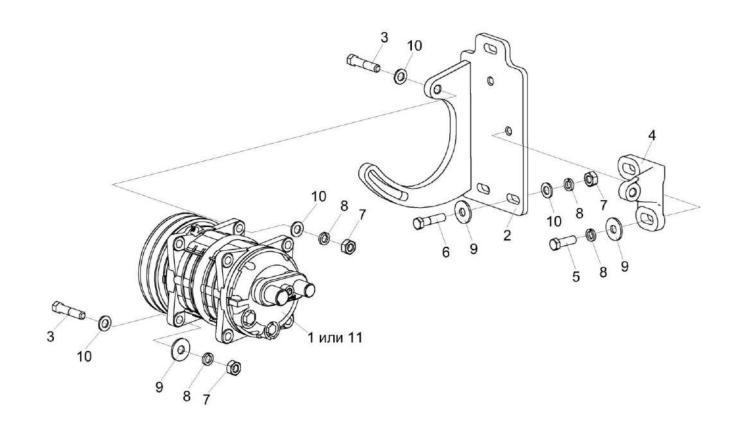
Установка компрессора КВС-7-0121030ВИ1 и КВС-80-7-0121060ВИ1
